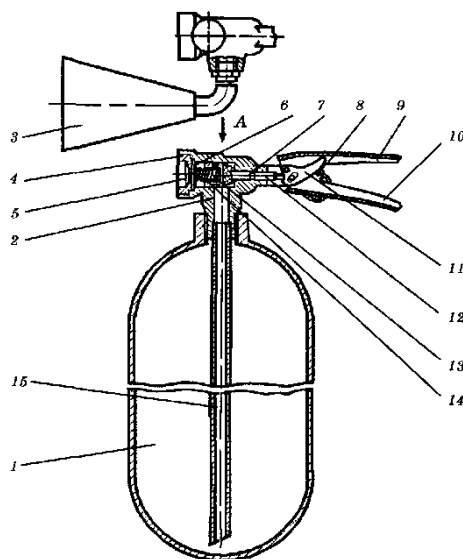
Вогнегасник вуглекислотний ВВК-2: 1 – корпус; 2 – голівка; 3 – розтруб; 4 – гайка; 5 – запобіжна мембрана; 6 – шайба; 7 – кільце ущільнювальне; 8 – запобіжна чека; 9 – важіль керування клапаном; 10 – ручка; 11 – кулачок; 12 – шток; 13 – клапан; 14 – пружина; 15 – трубка сифонна
